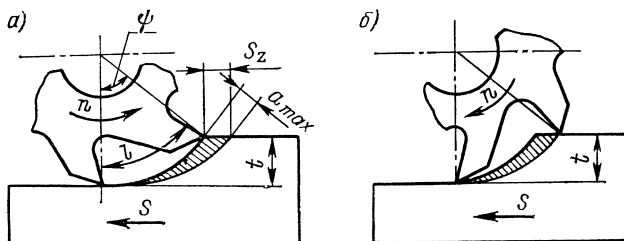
Схемы фрезерования: а — против подачи; б — попутное
